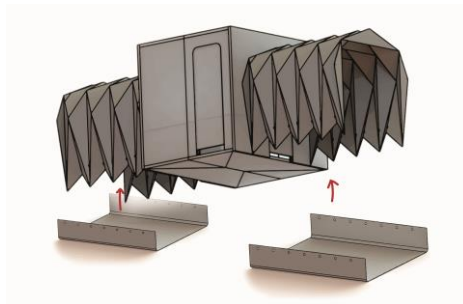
Paso 5. Ensamblaje de la lona a la estructura extensible
